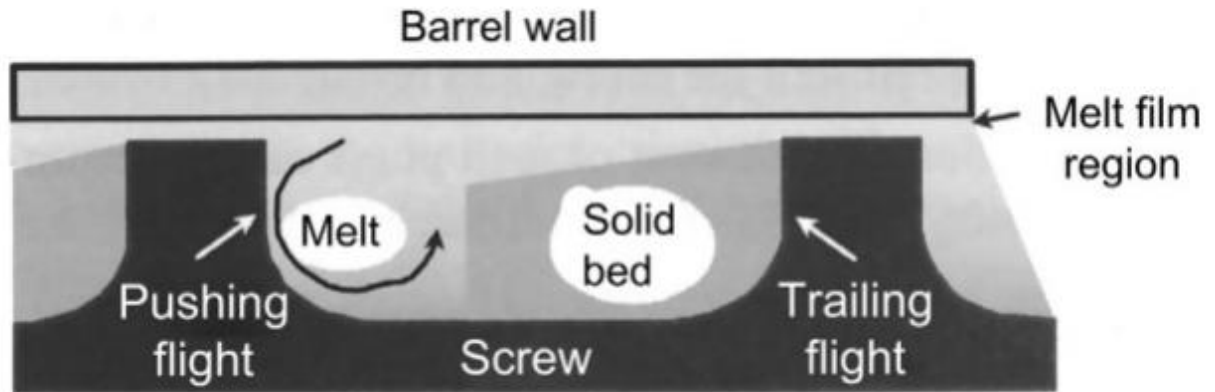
Плавлення полімерного матеріалу та утворення твердого шару
